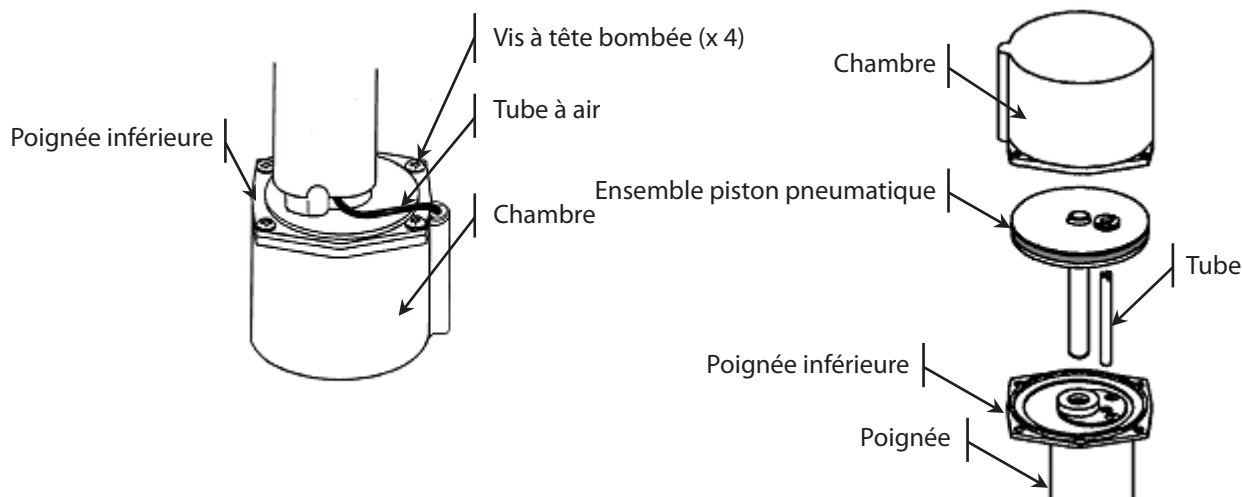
Retirer la chambre et l'ensemble Piston pneumatique
